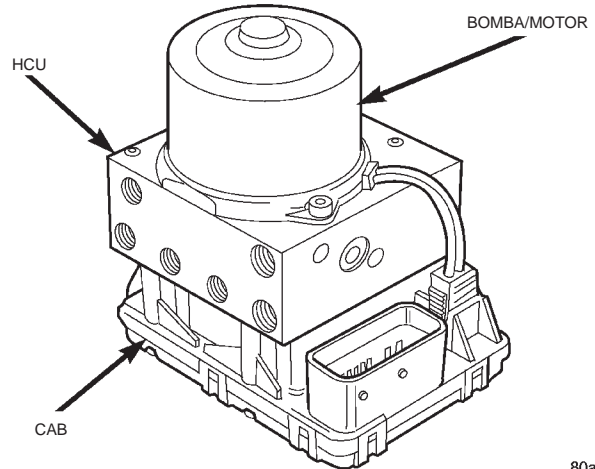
Bomba/motor de HCU del sistema Teves Mark 20
